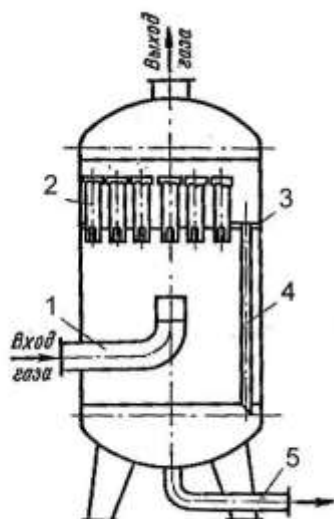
Схема сепаратора с прямоточными центробежными элементами.
